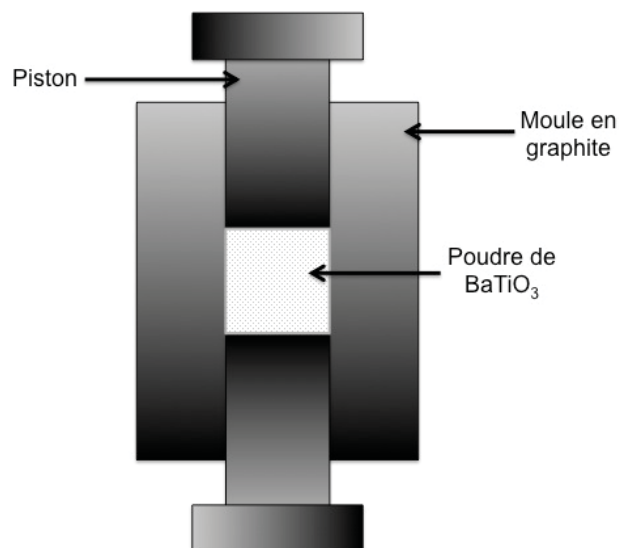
Schéma représentatif d'un ensemble pistons-moule-poudre pendant le frittage SPS
